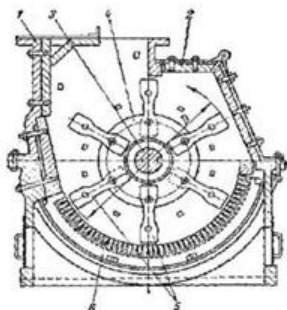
Молотковая дробилка - вид и схема работы:1-корпус; 2- отбойная плита; 3-вал;4-диск; 5-молотки;6-колосниковая решетка.
